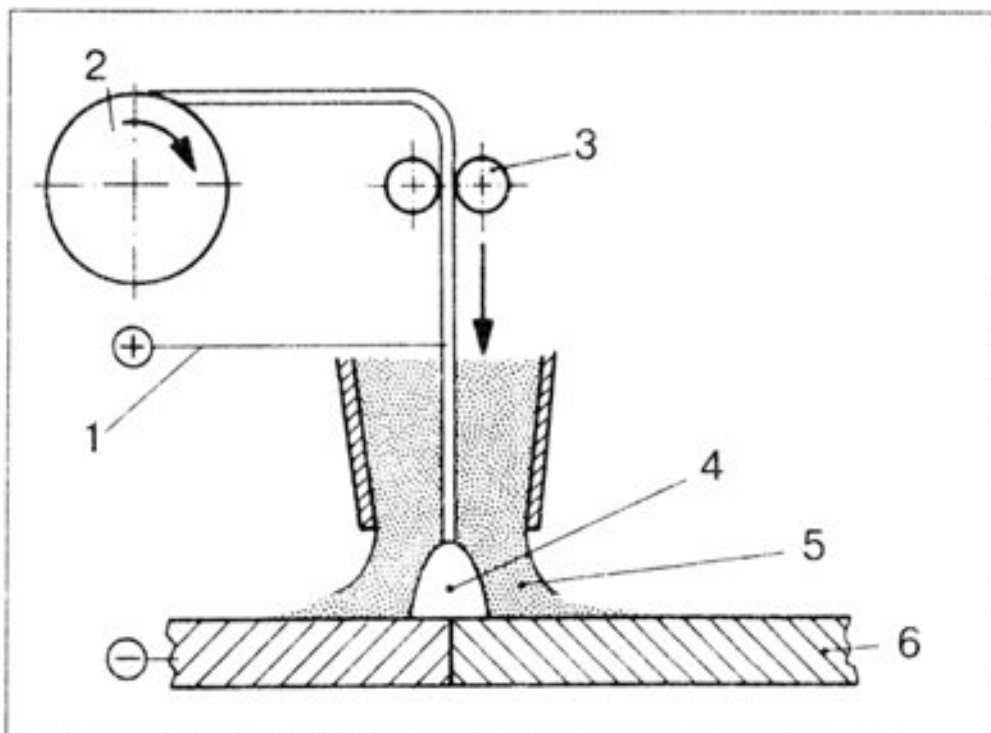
Схема процесса сварки в среде защитного газа: 1 – электрод; 2 – катушка с проволочным электродом; 3 – механизм подачи проволочного электрода; 4 – электрическая дуга; 5 – защитный газ; 6 - деталь
